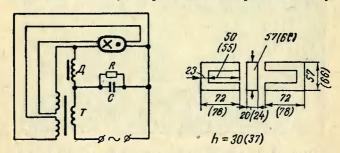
Принципиальная схема, коиструкция и размеры магнитопроводов аппаратов типа БЛ-1-40/220 и БЛ-1-80/220. В скобках показаны размеры магнитопровода для аппарата типа БЛ-1-80/220.
